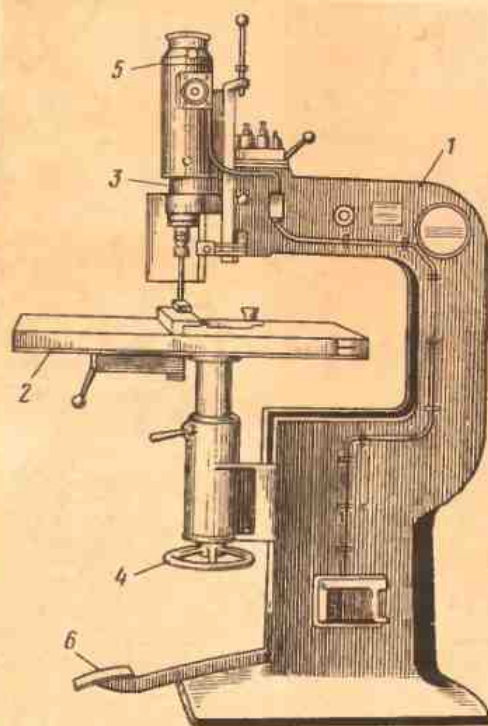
Многошпиндельный фрезерно-копировальный станок:
